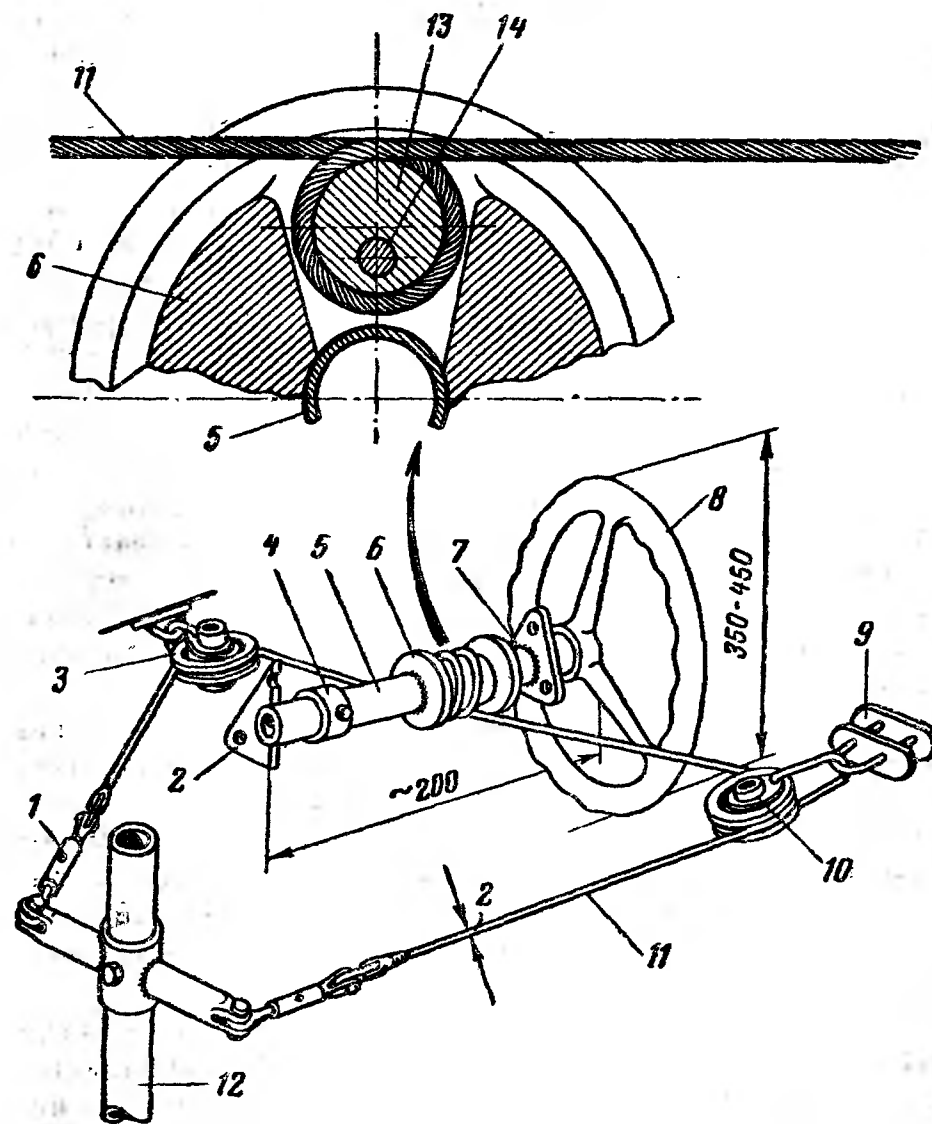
Схема тросового управления аэросаней «ОСГА-4» и узел крепления троса на барабане. 1 — тандер (резьбовая муфта для натяжения троса); 2, 7 — подшипники трубы рулевого колеса; 3 — самоустанавливающийся ролик; 4 — упорное кольцо; 5 — труба рулевого колеса; 6 — барабан для намотки троса; 8 — рулевое колесо; 9 — узел крепления ролика; 10 — ось ролика; 11 — трос управления; 12 — передняя коленка; 13 — эксцентричный зажимной ролик; 14 — болт-ось зажимного ролика.
